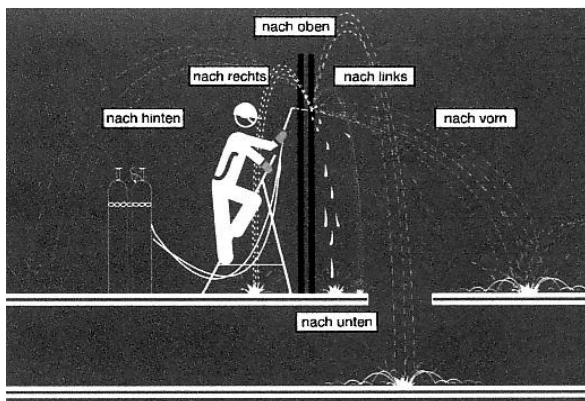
Ausbreitungsverhalten heißer Partikel bei schweißtechnischen Arbeiten
